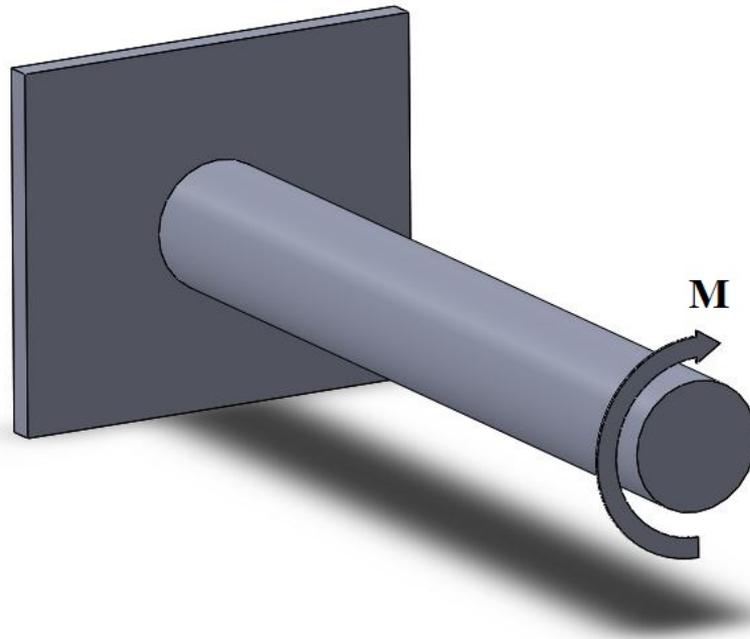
Demonstração da aplicação de momento torçor em uma viga engastada-livre.
